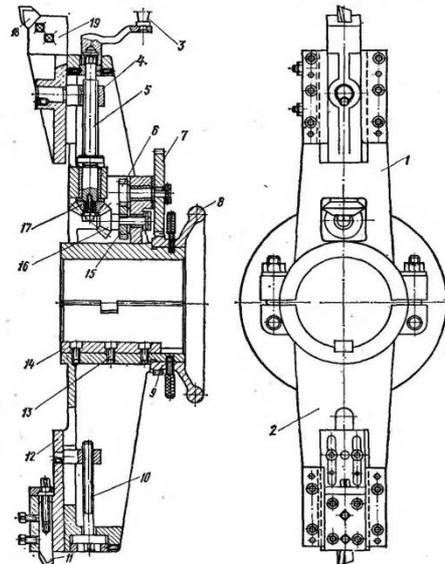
Расточный суппорт с маховиком и зубчатыми колесами
